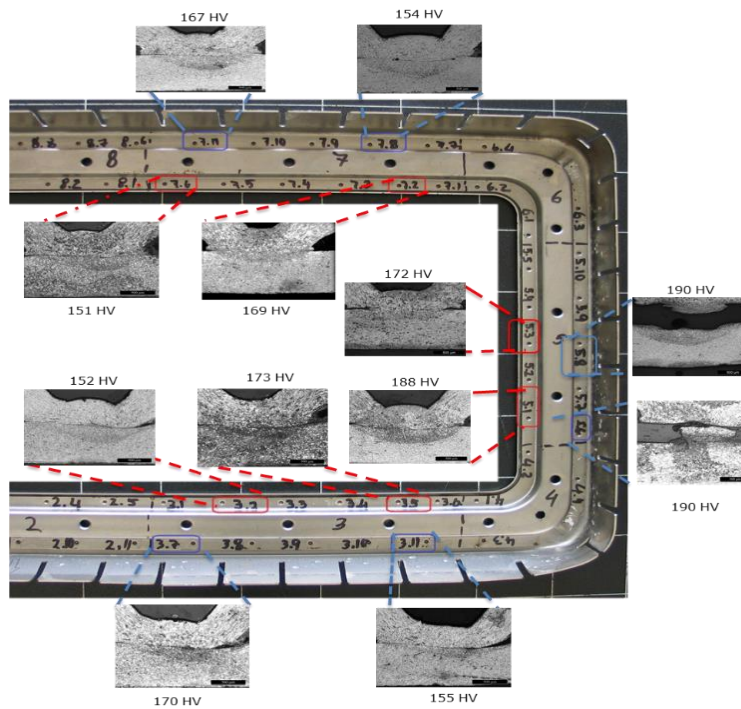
Mapa de soldaduras da peça F40/E25
